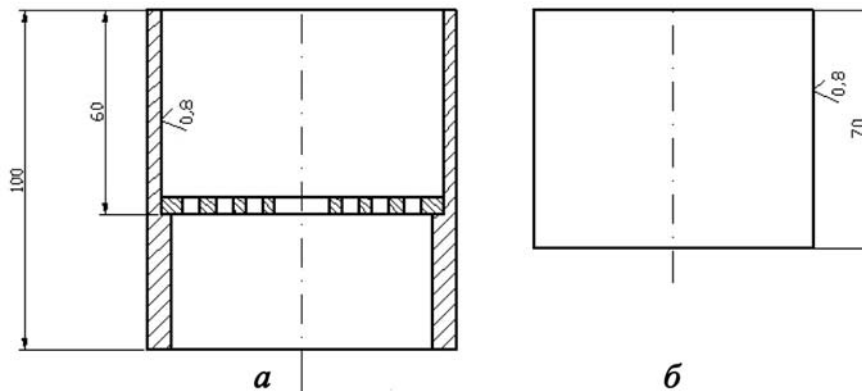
Деталі випробувального стенду для протискування фаршу через ґратки вовчка: а – гільза з установленою ґраткою; б – поршень.
